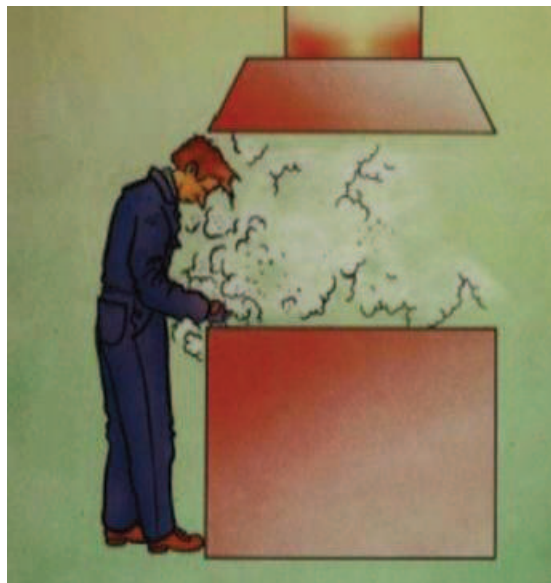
Campanas que no protegen, instaladas en el laboratorio de soldadura
